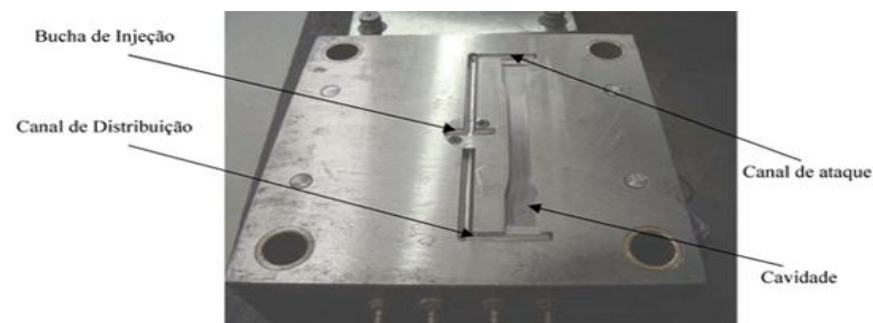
Imagem de uma placa móvel de um molde de injeção. Fonte: Bom e Kalin, 2008
